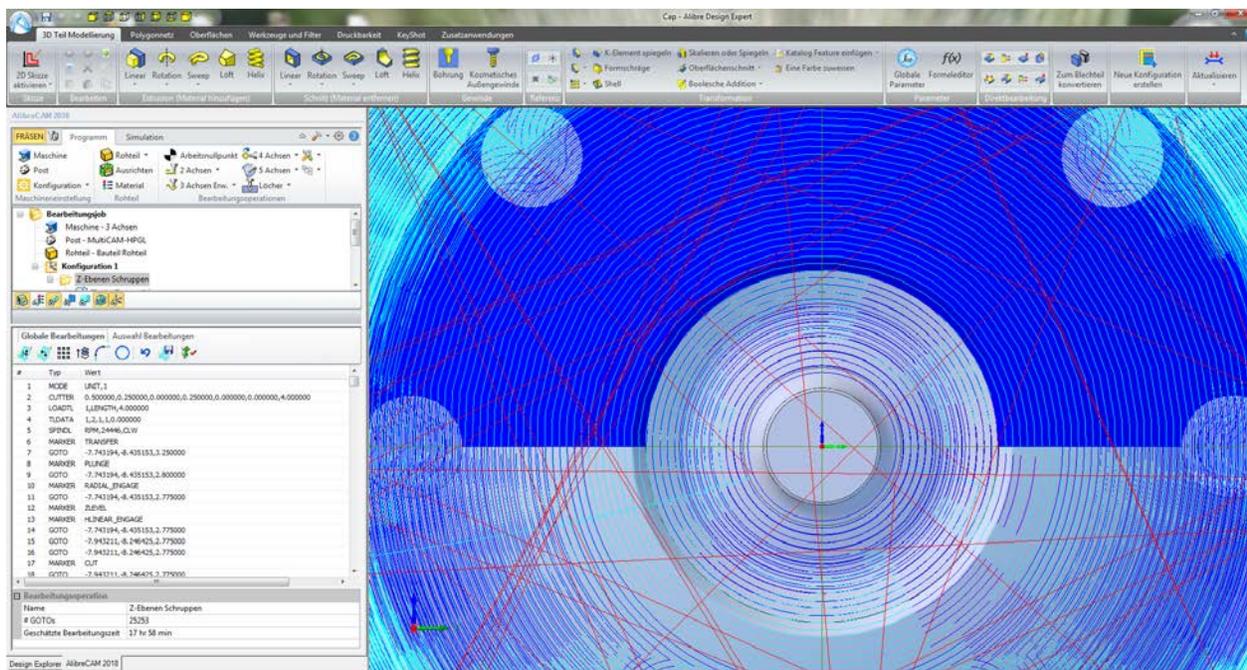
Bearbeitung eines Werkstücks – hier: Schruppen Z-Ebene
